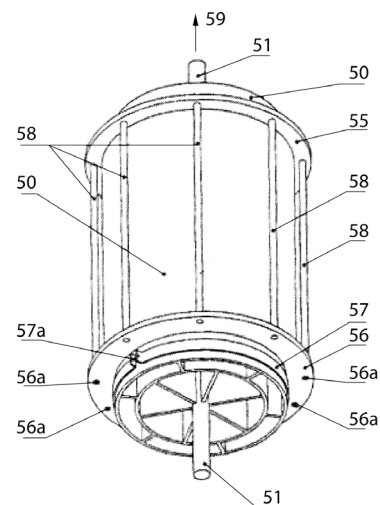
Вид в аксонометрии вертикально установленной и закрепленной трехслойной оболочки перед операцией выпрессовки из нее намоточной оправки 50 и сердечников 41
